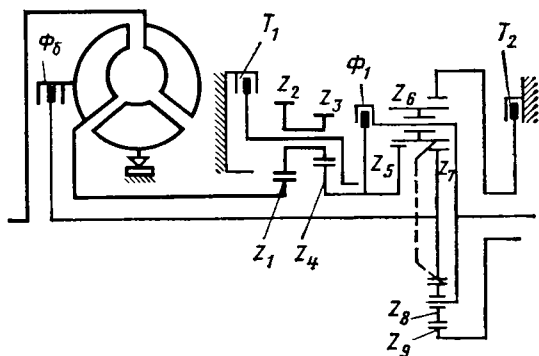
Схема четырехступенчатой гидромеханической передачи УВМВ-ЧЗМ-НАМИ ($z_1 - z_9$ — шестерни механического редуктора)
